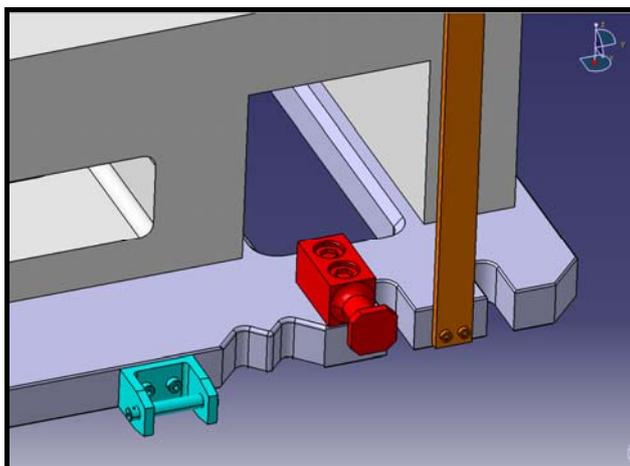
Doble hueco de posicionamiento para troquel estándar.
